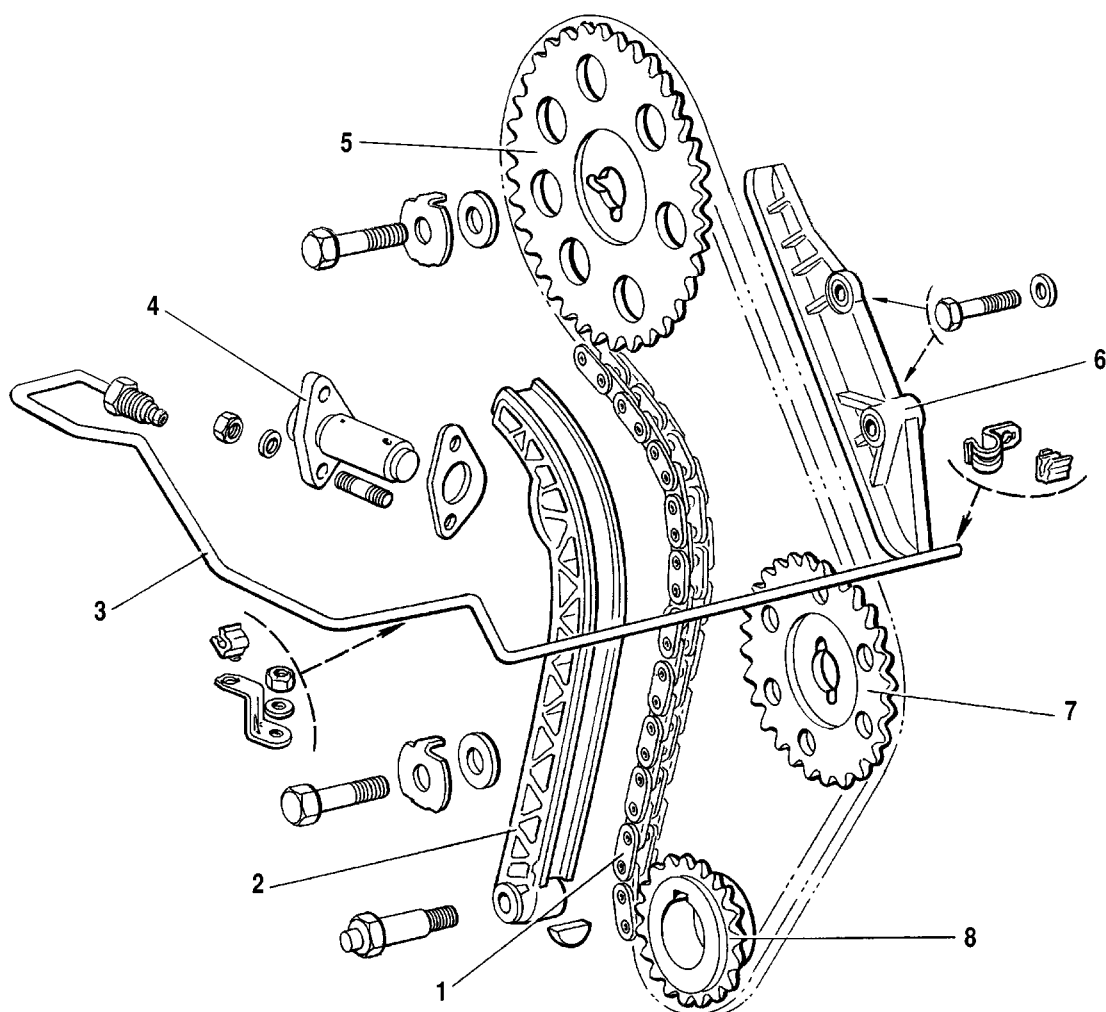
Bauteile der Kettenspannvorrichtung:
